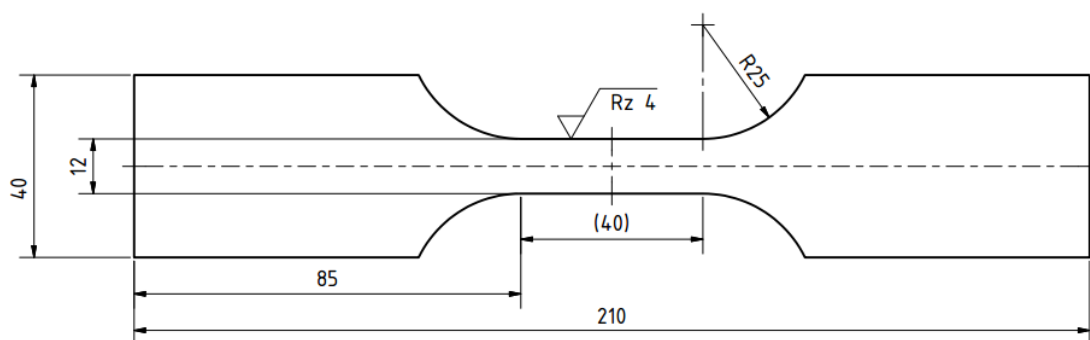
Эскиз образца для проведения испытаний сварных соединений на растяжение
